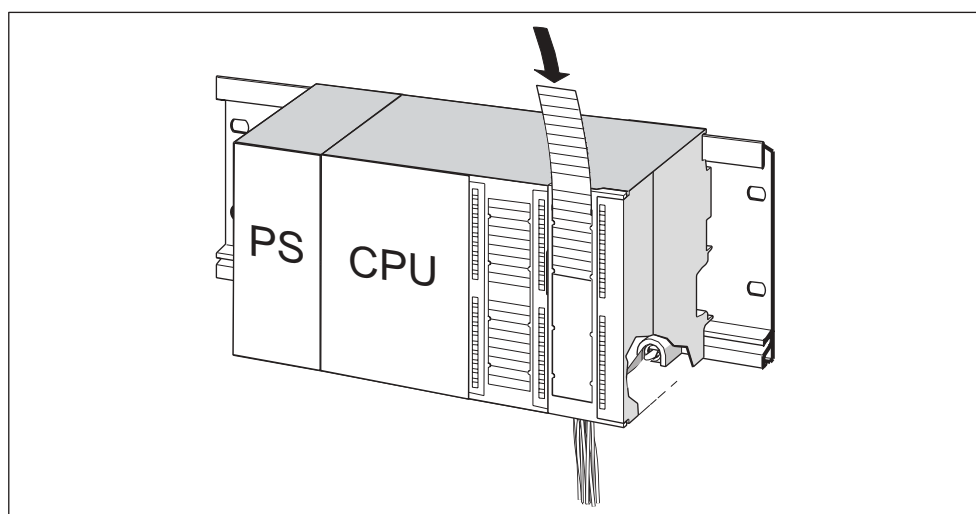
Introducción de las tiras de rotulación en la puerta frontal
